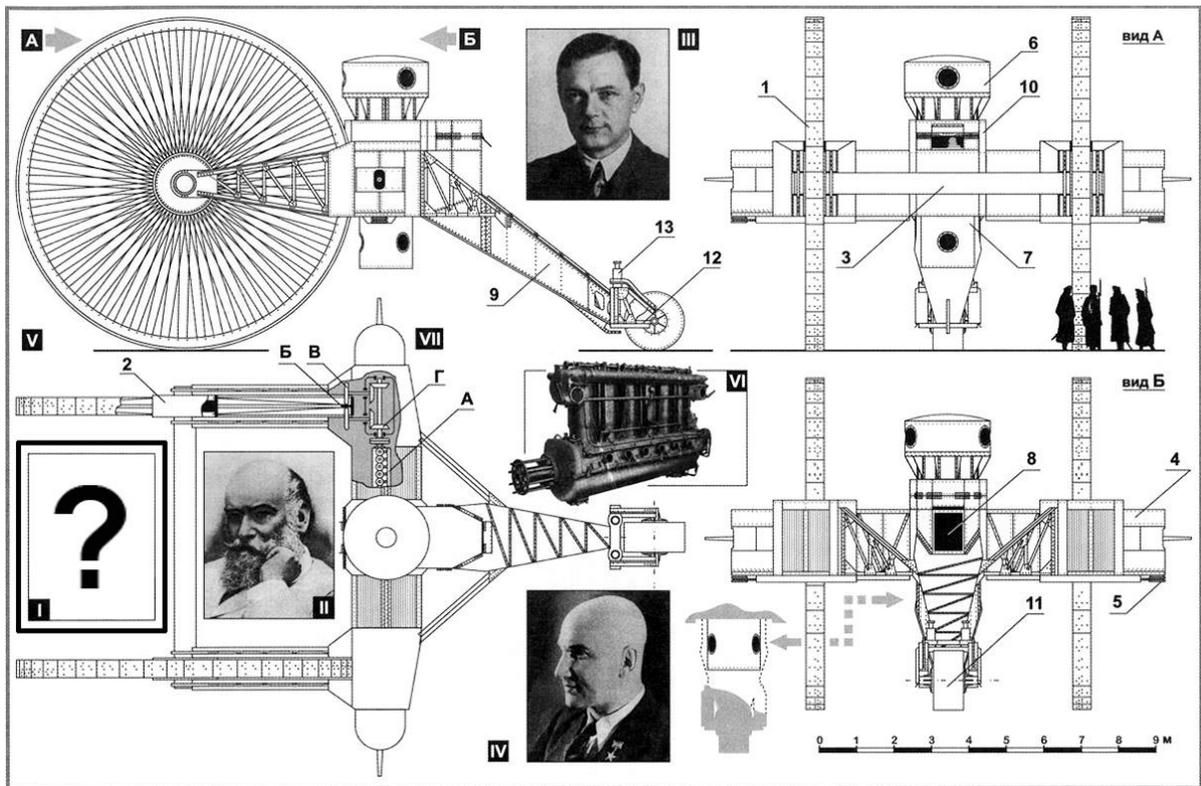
"Канонический" чертеж "Царь-танка" и фотопортреты людей,
